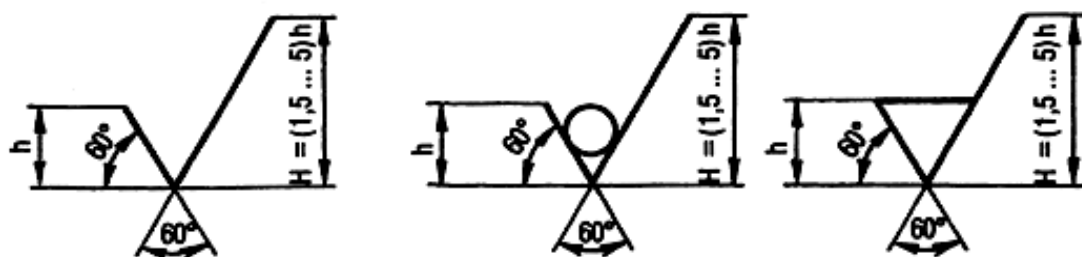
Знаки, применяемые для обозначения шероховатости
